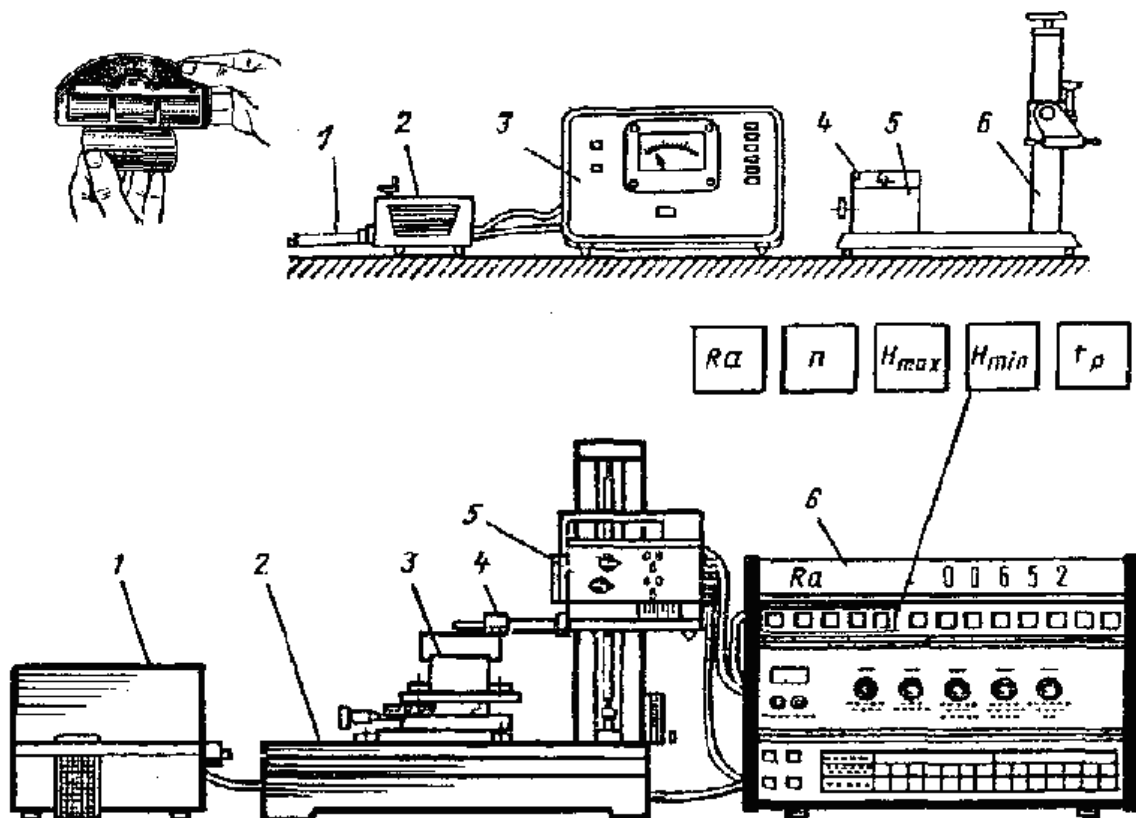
Профилометр модели 253: 1 – механотронный преобразователь; 2 – привод; 3 – электронный блок; 4 – столик; 5 – призма; 6 – стойка
